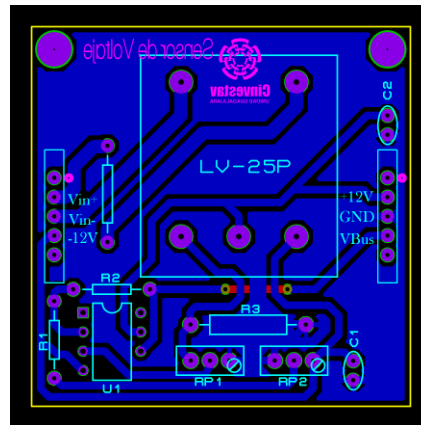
Sensor de Voltaje en PCB Di. Pr.
